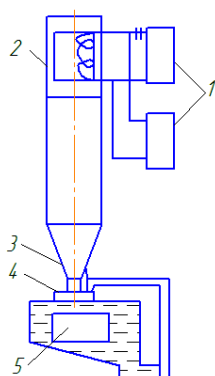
Схема ультразвуковой обработки: 1 – силовой агрегат; 2 – магнитострикционный элемент; 3 – рабочий инструмент вибратора; 4 – профилирующий наконечник инструмента; 5 – заготовка.
